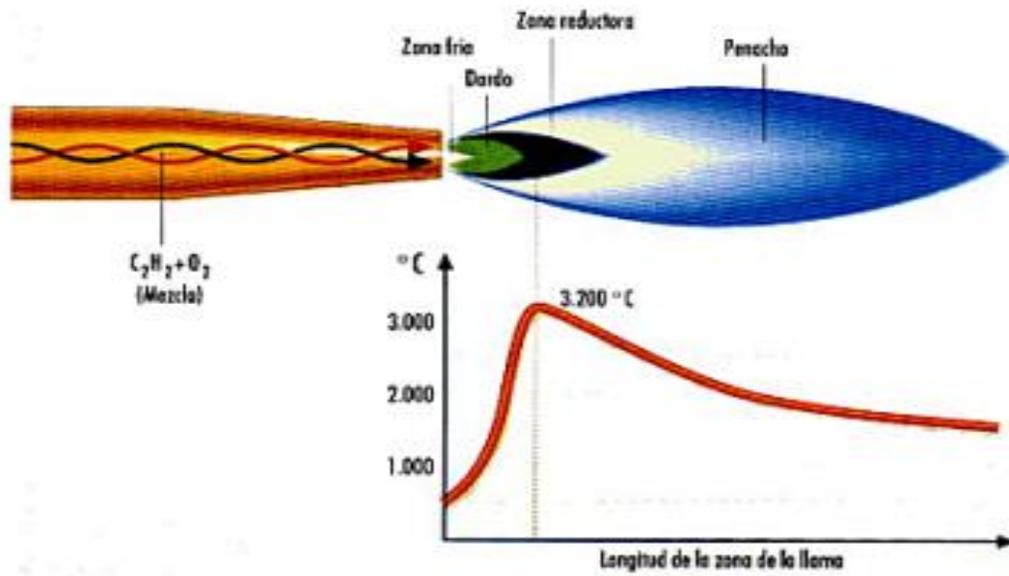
Flama de la soldadura acetilénica.
